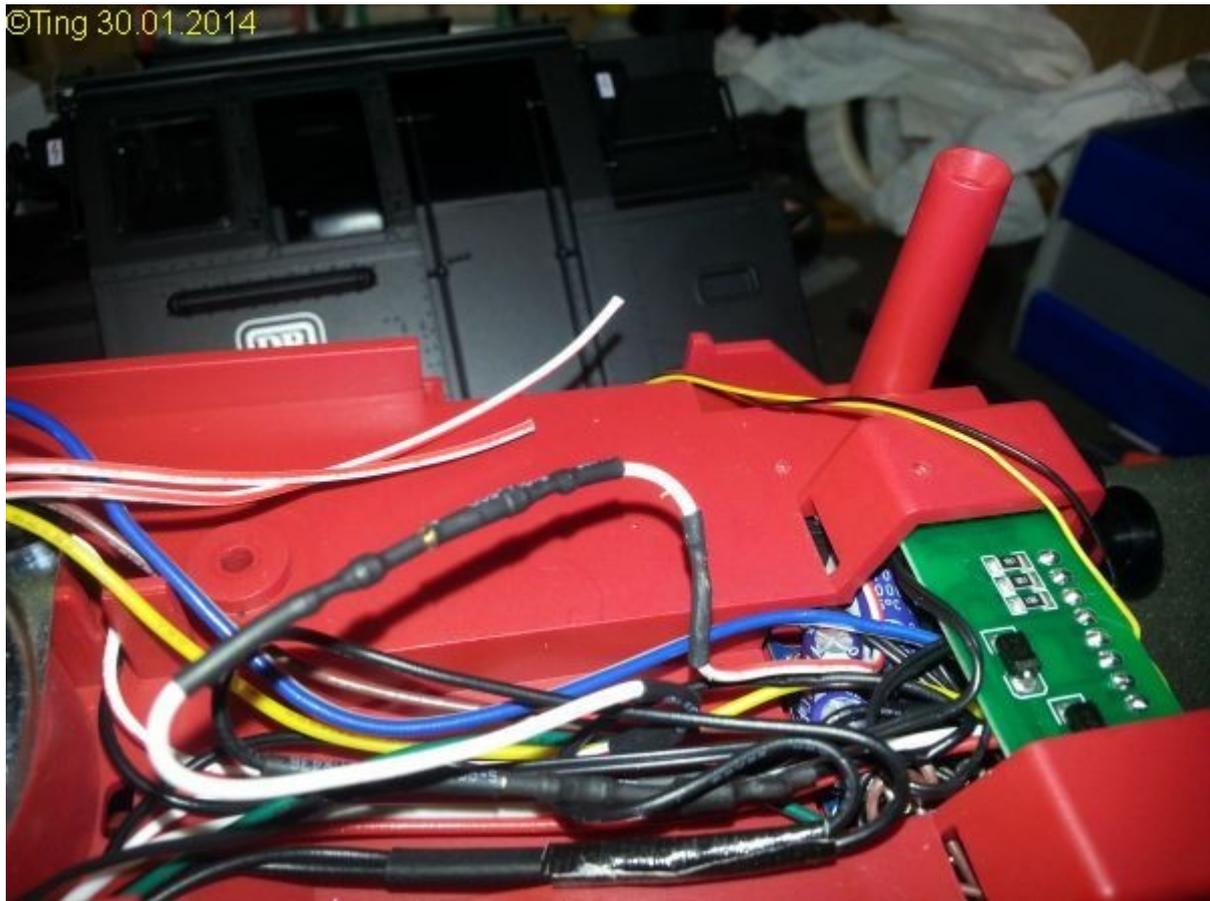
Wieder angelötetes Kabel für Triebwerksbeleuchtung
